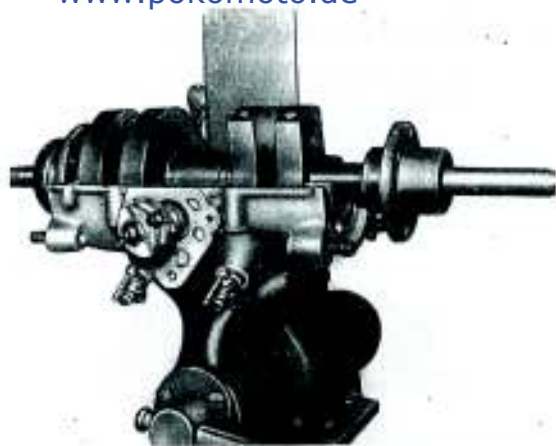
Flansch am magnetseitigen Wellenstumpf aufstecken
